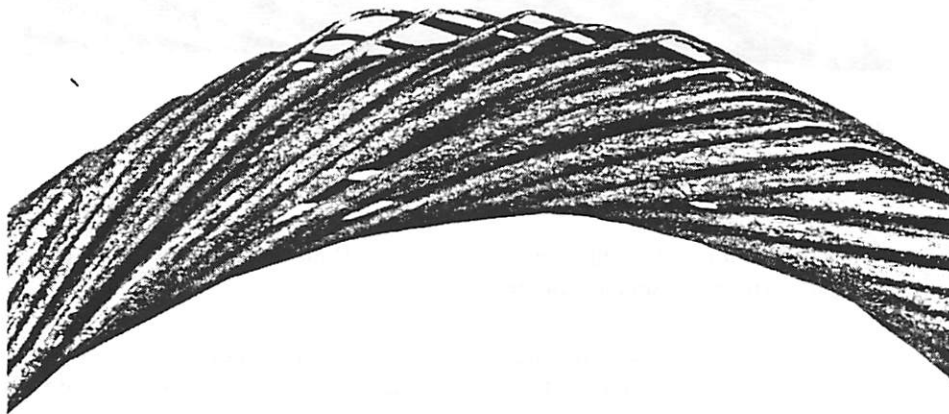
Drahtseil mit durch Korrosion und Abrieb gelockerten Drähten
